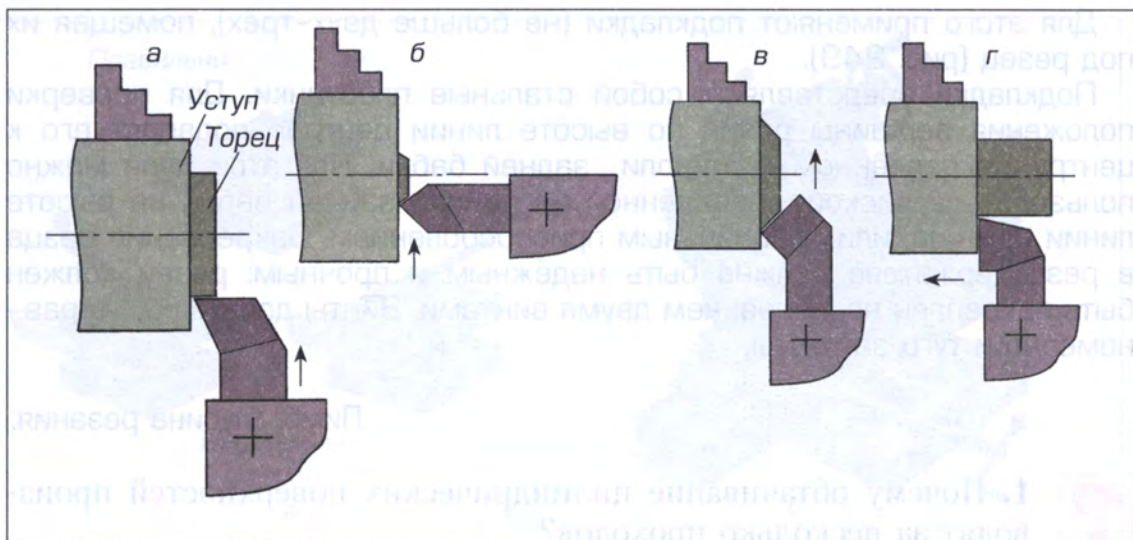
Токарная обработка торцевых поверхностей и уступов:
